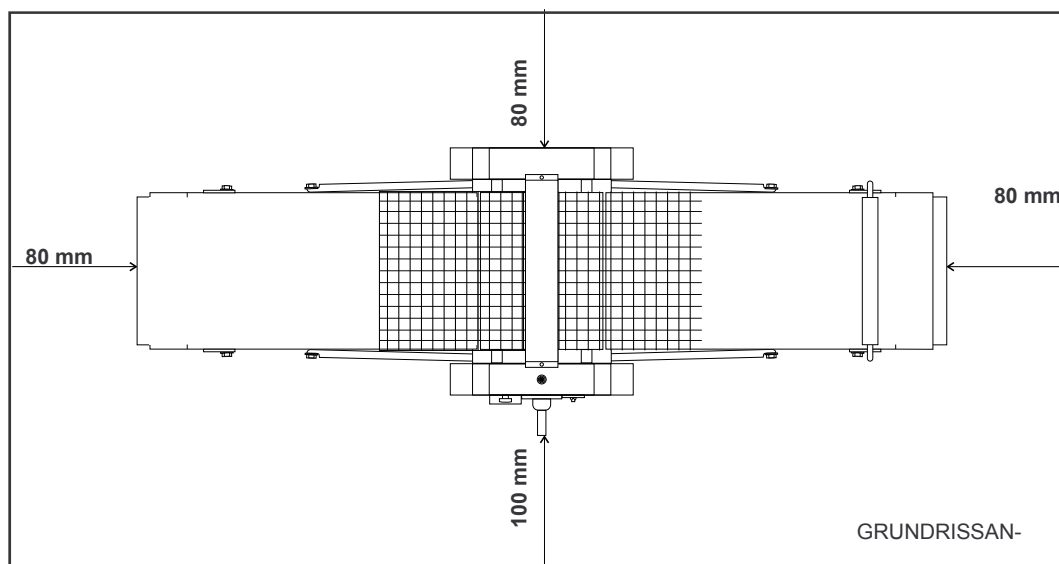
(MINDESTABMESSUNGEN FÜR DIE PLATZIERUNG DER MASCHINE)
